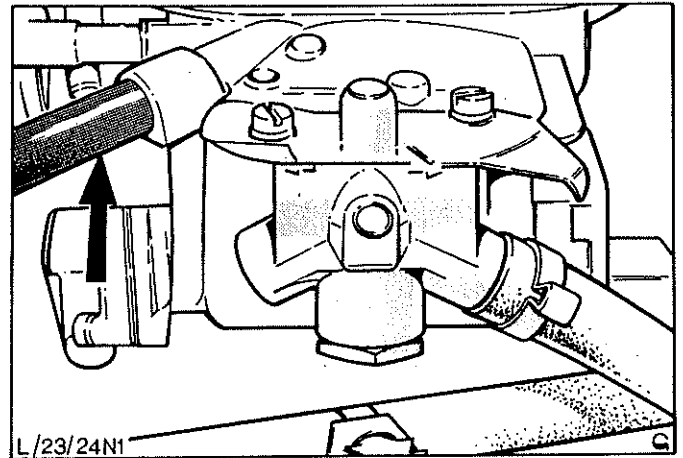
Gemischzufuhrschlauch zum Verzögerungsventil (nur bei Fahrzeugen für Schweden)
